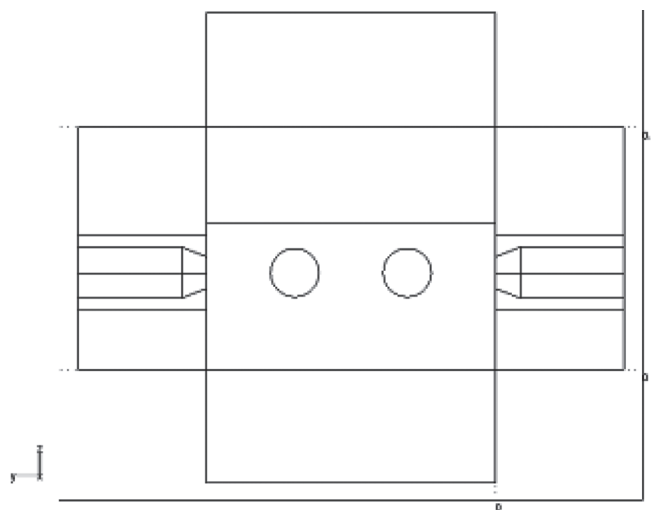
Чертеж нагревательной печи скоростного струйного нагрева металла (горцевой разрез)
